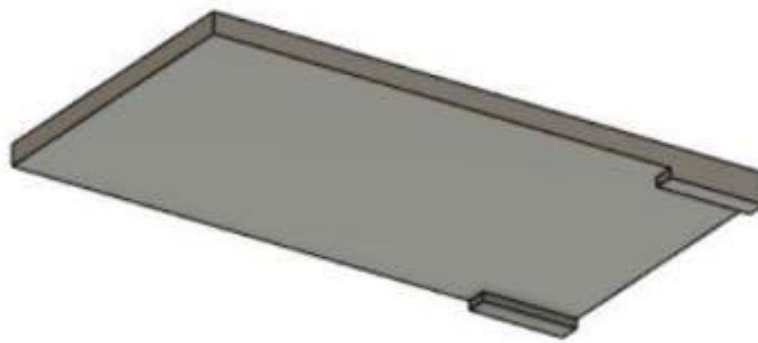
Кришка для верхньої частини основи корпусу пристрою
